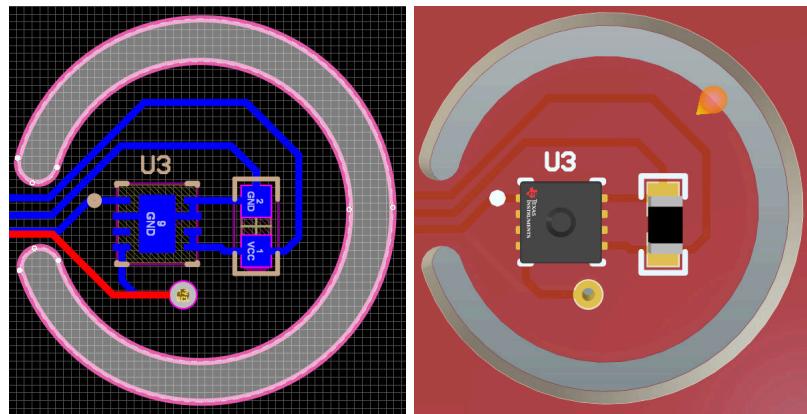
HDC3020 PCB 布局示例，在 HDC3020 周围开有槽口
